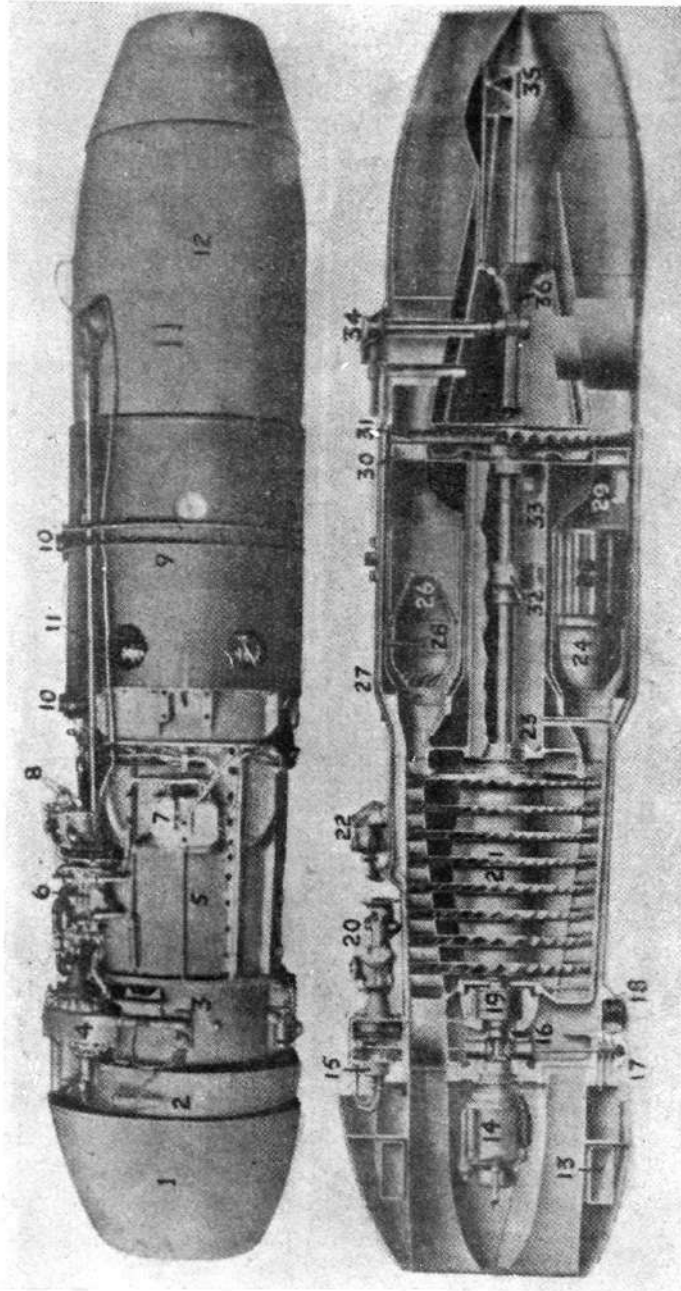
Turborreactor alemán de compresor axial Junkers-Jumo 004-B. 1, capotaje de refrigeración; 2, tanque de aceite; 3, cárter de entrada; 4, caja auxiliar de engranajes; 5, cárter del compresor; 6, servomotor; 7, dispositivo de encendido; 8, palanca de mando; 9, cárter exterior; 10, puntos de sujeción del motor; 11, eje de mando del cono móvil de la tobera de la salida; 12, cárter de la tobera de salida; 13, tanque anular de aceite; 14, motor de arranque; 15, bomba de inyección; 16, engranaje auxiliar de puesta en marcha; 17, bomba de aceite lubricante; 18, filtro de aceite; 19, cojinete delantero del compresor; 20, regulador del régimen; 21, rotor del compresor; 22, filtro de aceite; 23, cojinete posterior; 24, tubo de llamas; 25, manguito de las cámaras de combustión; 26, mezclador de rejilla de los gases de combustión; 27, cámara de combustión; 28, inyector; 29, cárter de entrada de la turbina; 30, director de la turbina; 31, rotor de la turbina; 32, cojinete anterior de la turbina; 33, fém posterior con bomba recuperadora de aceite; 34, engranajes de mando del cono móvil; 35, cono móvil en sentido longitudinal, a fin de poder variar el área de la tobera de salida; 36, soporte del cono móvil.
